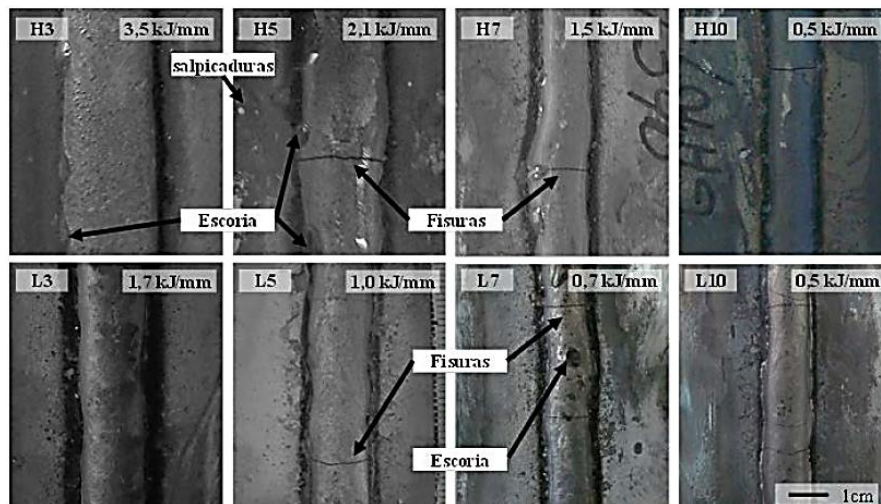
Vista superior de los cordones bead on plate. Soldados con Ar-20%CO₂
